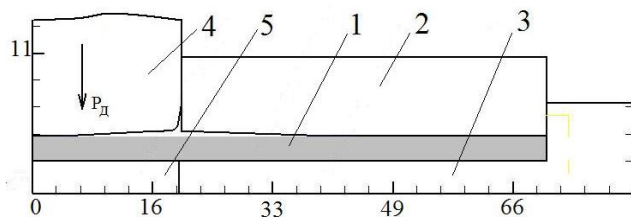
Розрахункова схема формування отвору і профілювання заготовки
